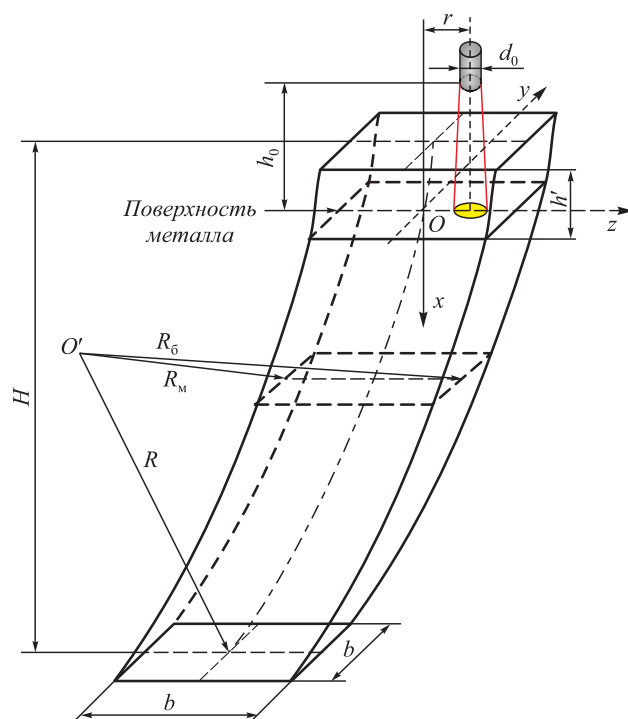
Основные размеры сортового кристаллизатора при разливке открытой струей металла и выбранная система координат
